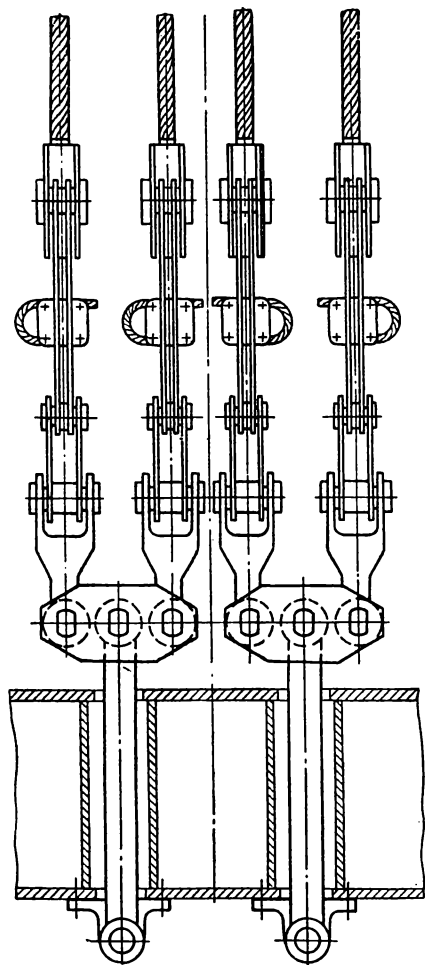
Общий вид двухбалансирующего подвешного устройства для подъемного сосуда четырехканатной подъемной установки со шкивом трения
